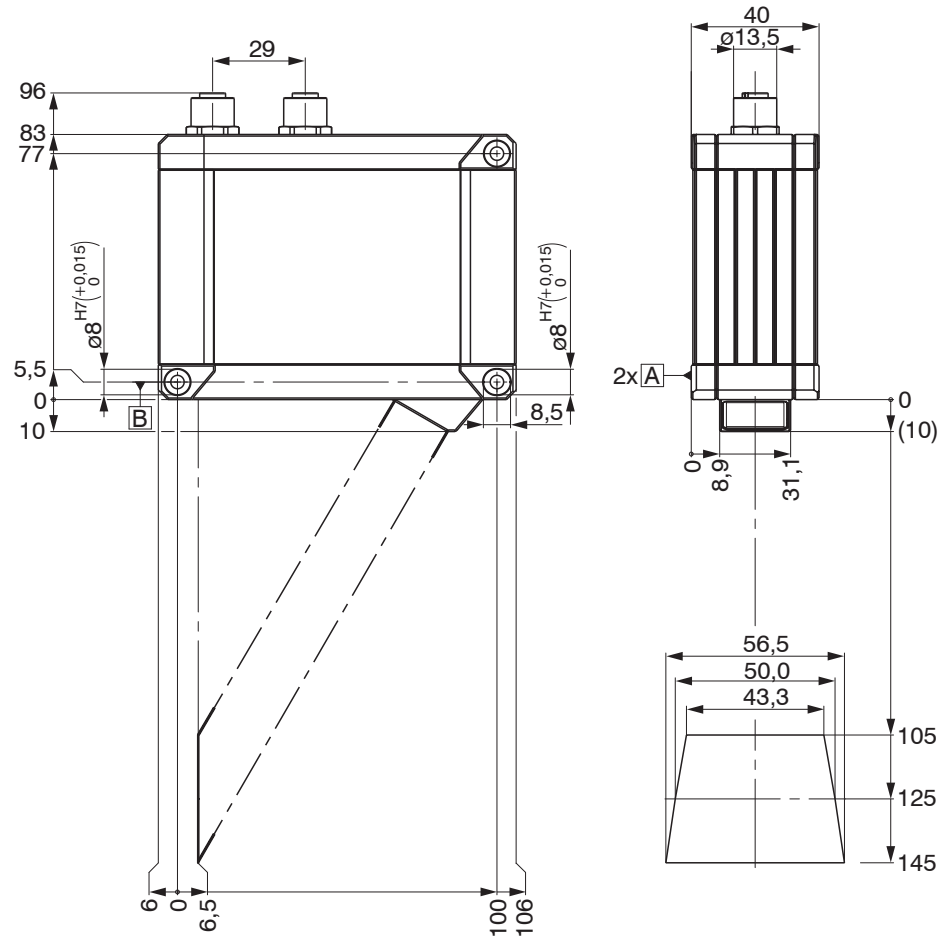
Maßzeichnung Sensor scanCONTROL 30xx-50
